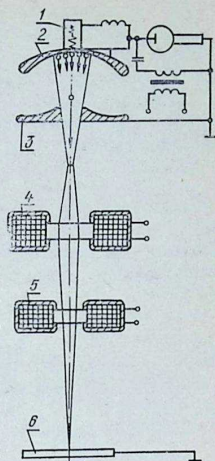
Схема установки для сварки электронным лучом:
